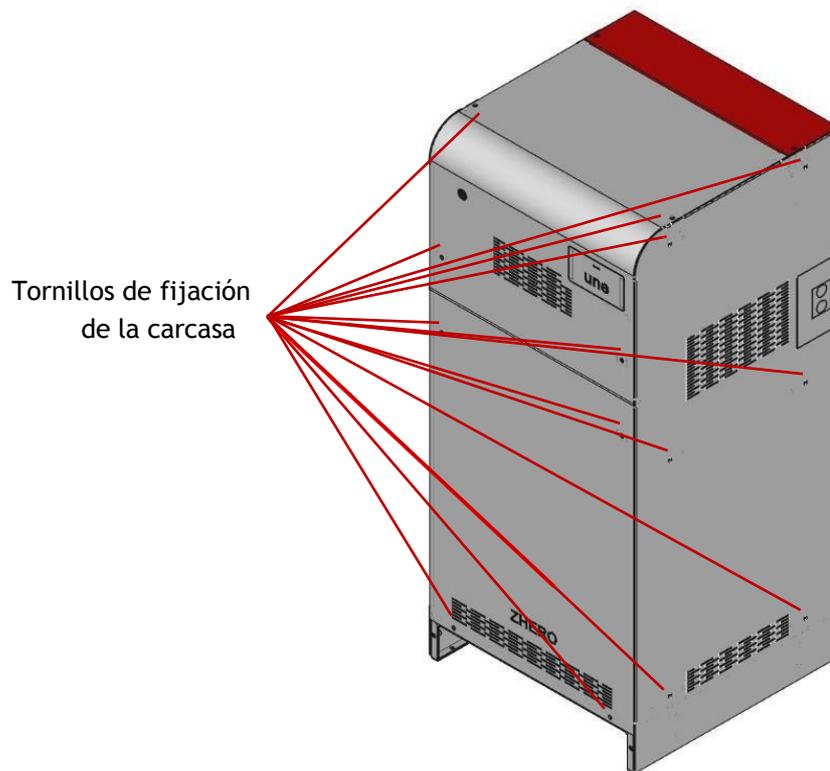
Posición de los tornillos de cabeza cilíndrica para desmontar los paneles
